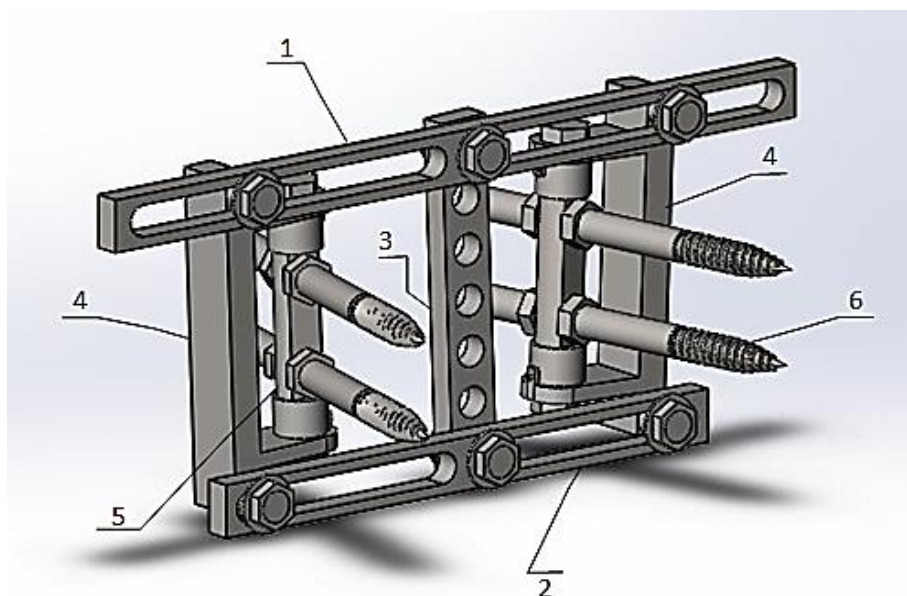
Модель аппарата наружной фиксации: 1 – верхняя длинная балка; 2 – нижняя короткая балка; 3 – балка укосина; 4 – удерживающие планки; 5 – цилиндрические поворотные крепежи; 6 – стержни типа Шанца с резьбой
